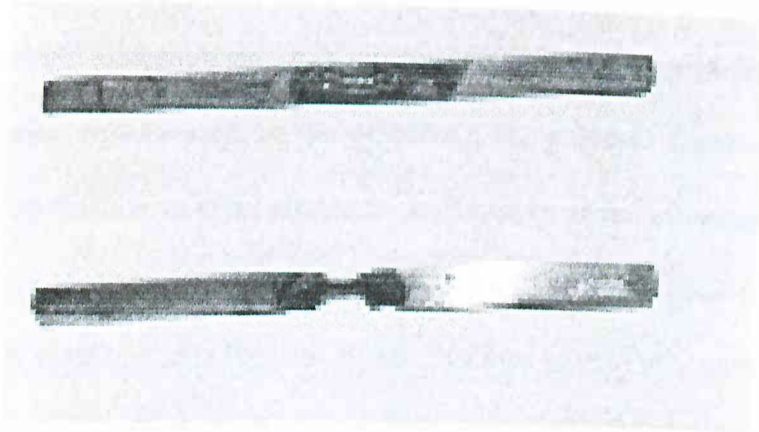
Comparação visual de um entalhe usinado com NaCl com a peça padrão; (a) Peça com dois entalhes usinados; (b) Entalhe padrão.
